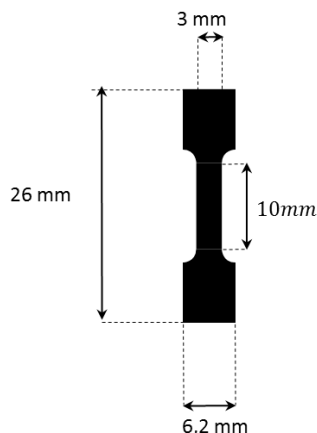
dimension des éprouvettes de traction obtenue à partir des pastilles frittées dans la machine de compression.
